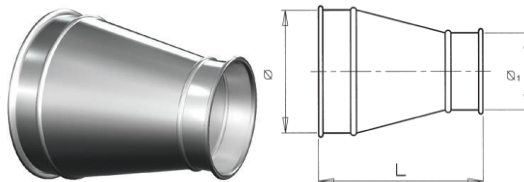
Cone de redução QFS (QFS Oil Mist & Cutting Fluid)
